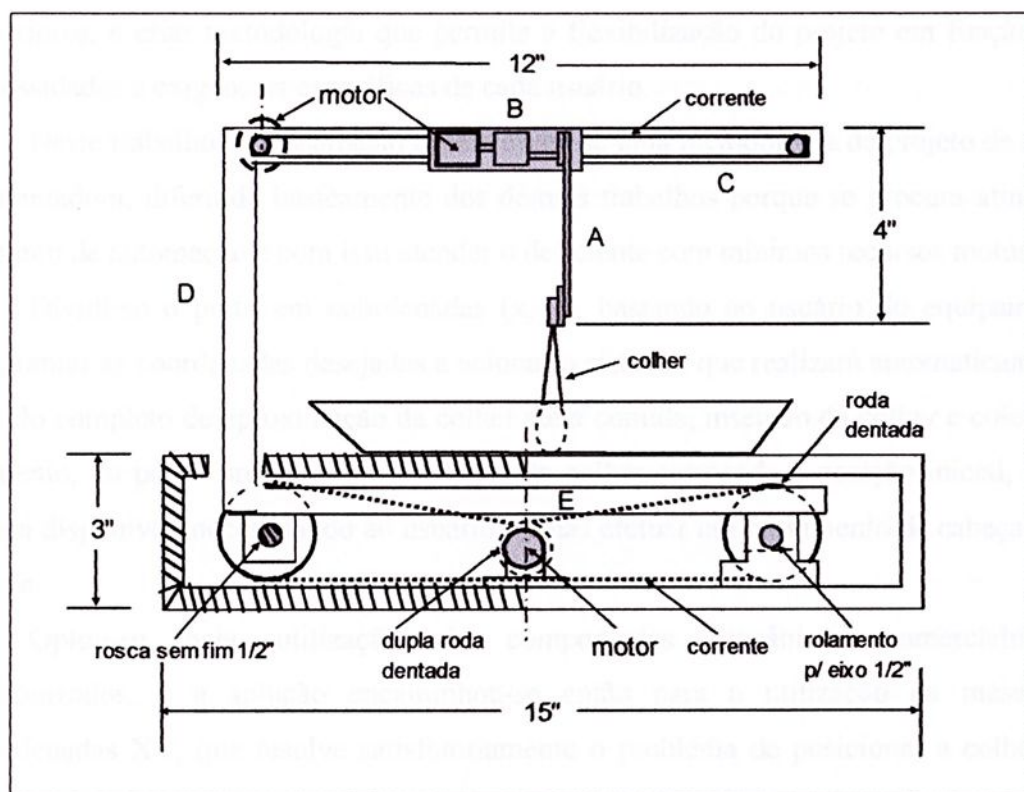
CO. Jones Feeder – Vista Frontal.
